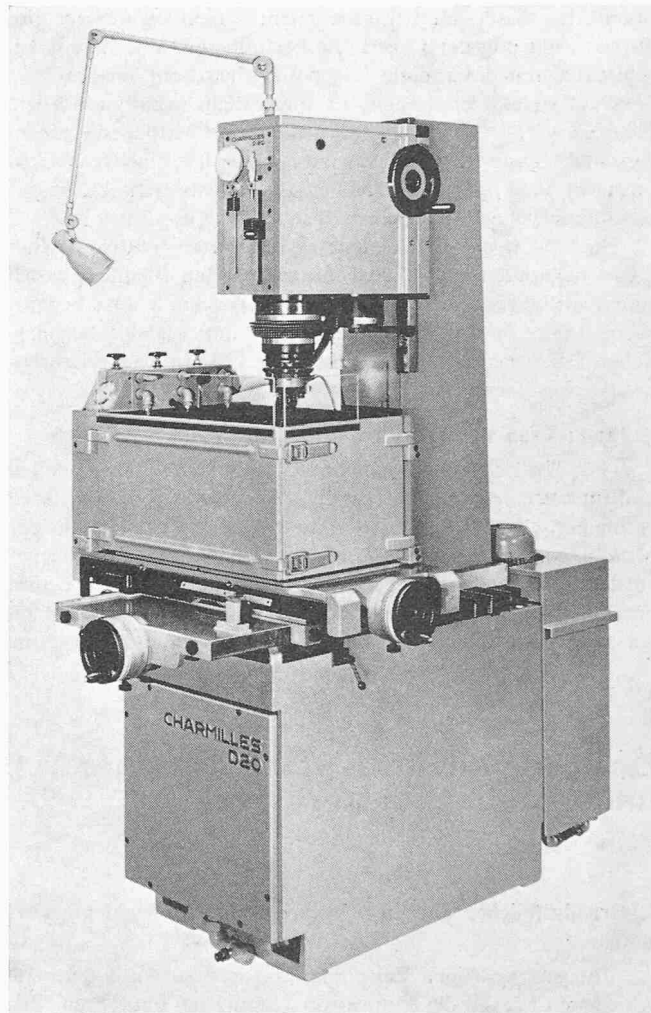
Funkerosions-Werkzeugmaschine Charmilles D 20
